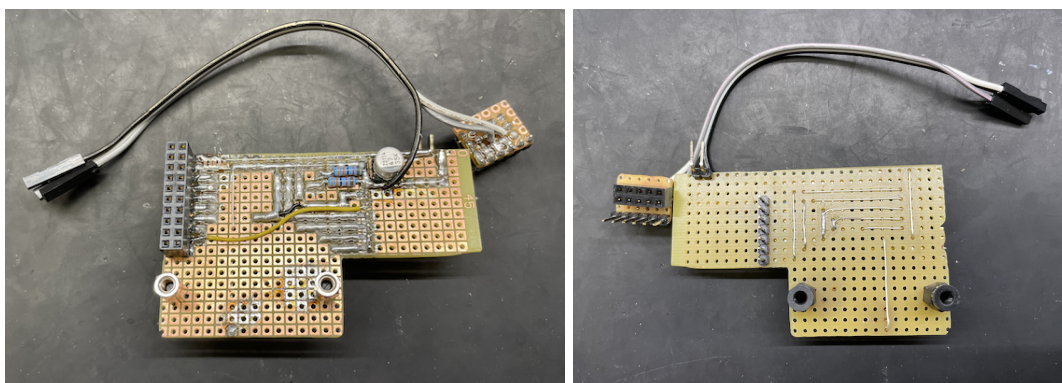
Přípravek DCCapSens – Přední a zadní část PCB pro připájení kondenzátorů
